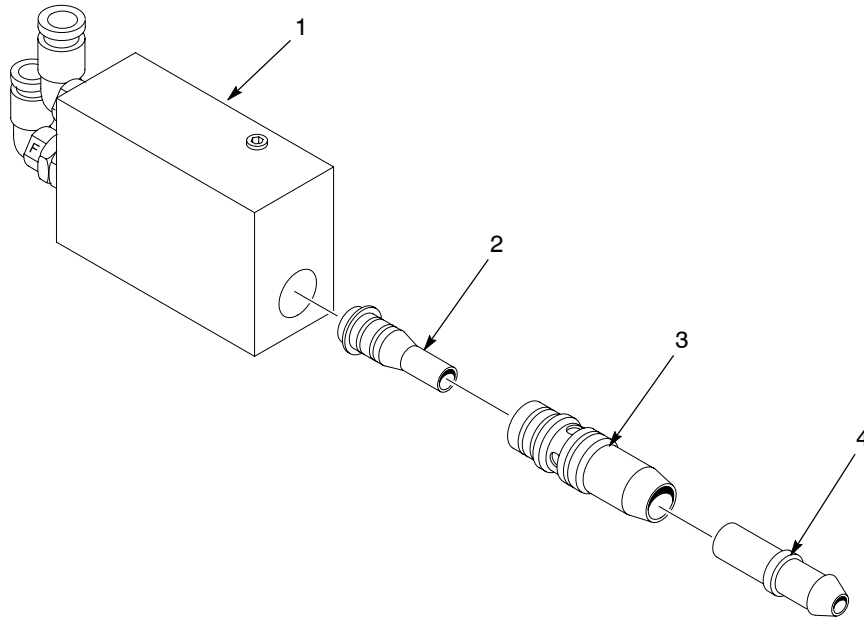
Venturihals für Behälterbeschichtung und Pulverschlauchadapter installieren
